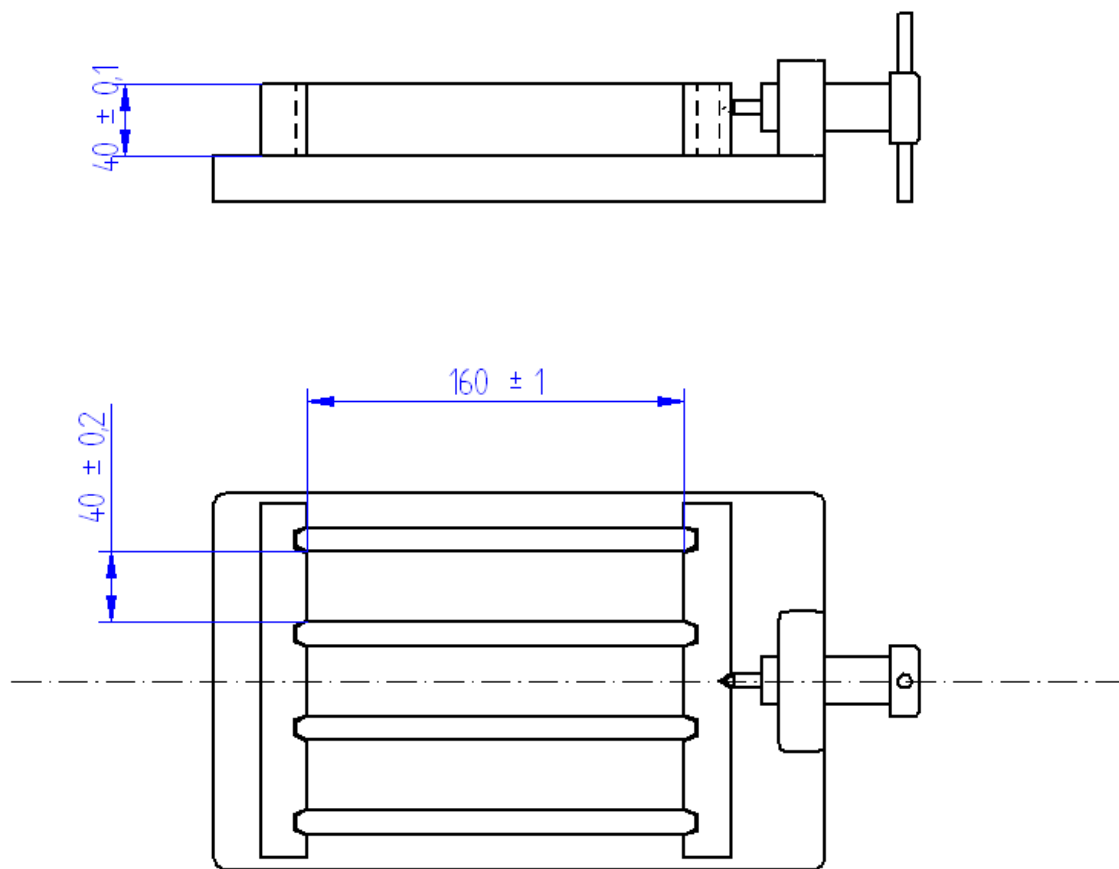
Misure e tolleranze dimensionali dello stampo in mm
